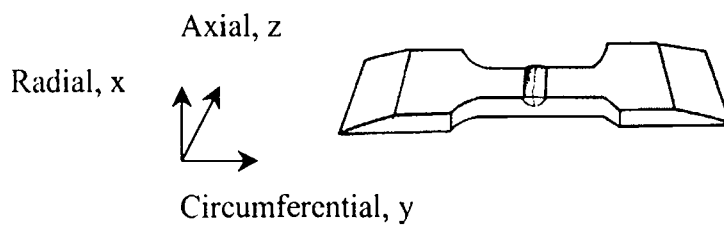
Esquema de las probetas C_1 - C_6 con ampolla atravesando el ancho en forma uniforme, lo que determina que la fisura sea through wall.
